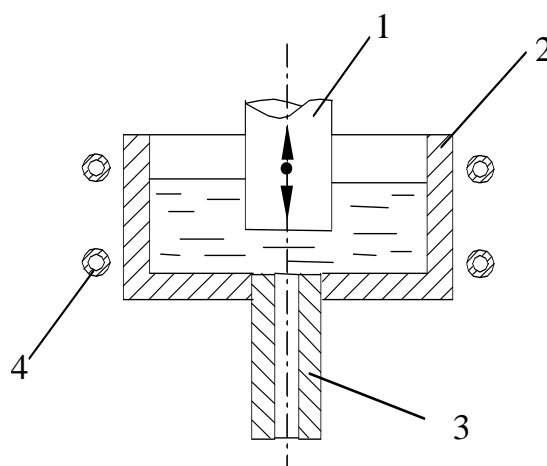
Ультразвуковой паяльник с дозирующим устройством: 1 – излучатель ультразвука; 2 – камера для припоя; 3 – капиллярная трубка; 4 –нагреватель
